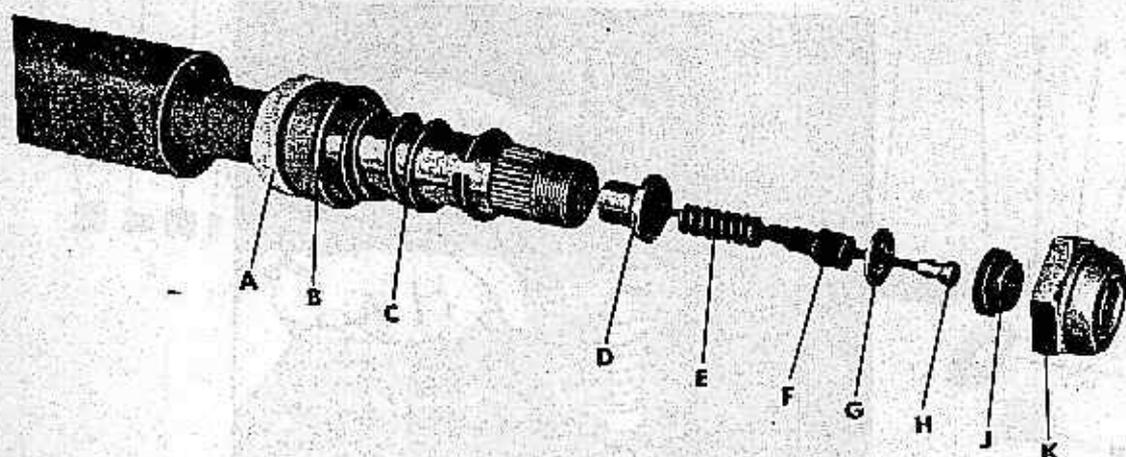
Ensemble du bouton de contact (vue éclatée)
